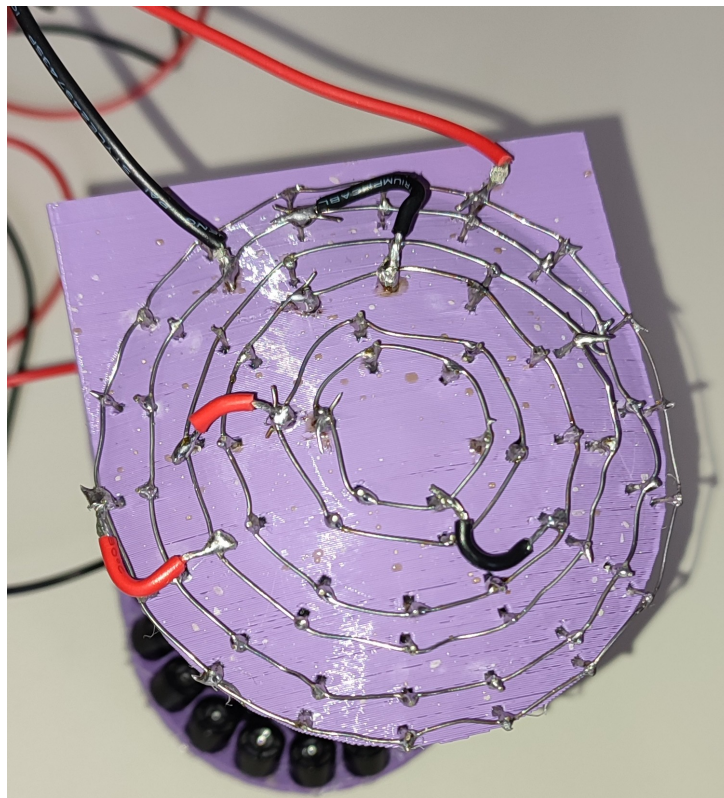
Soudure des fils d'alimentation des anneaux
